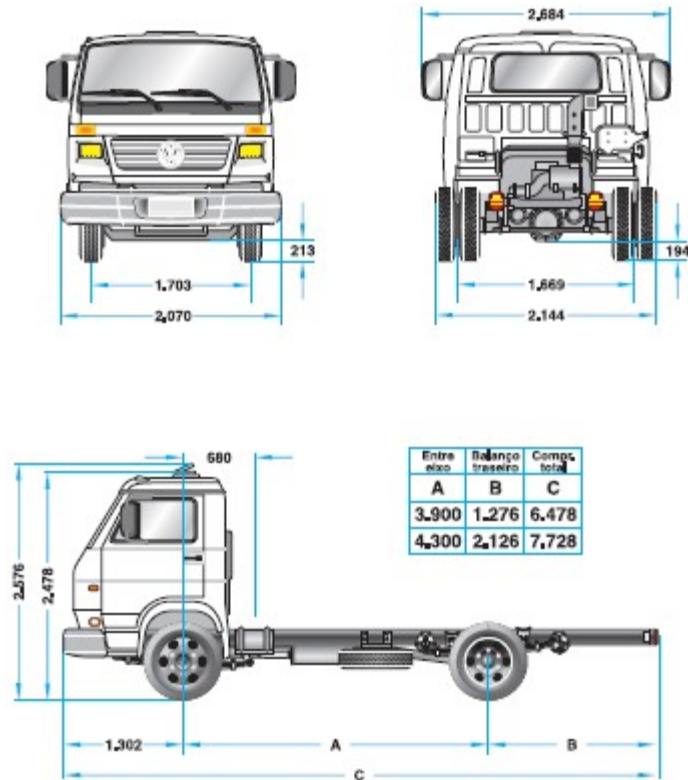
Dimensões Principais (mm) WV Worker 13-180
